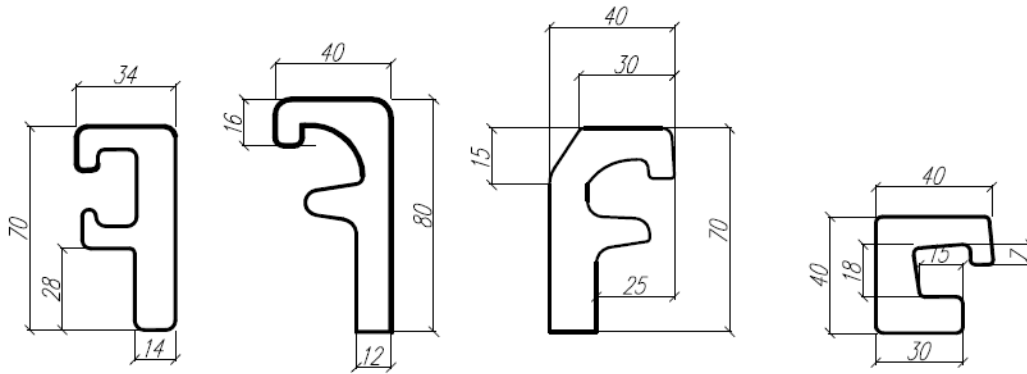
б. Крайний несущий металлический стоечный спецпрофиль
